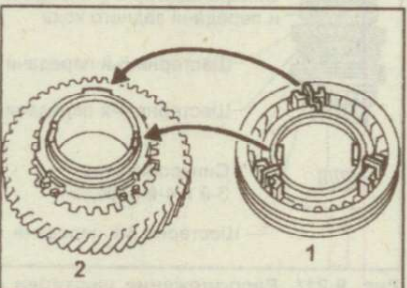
Установка синхронизатора (1) передачи заднего хода на шестерню (2) 5-й передачи первичного вала
